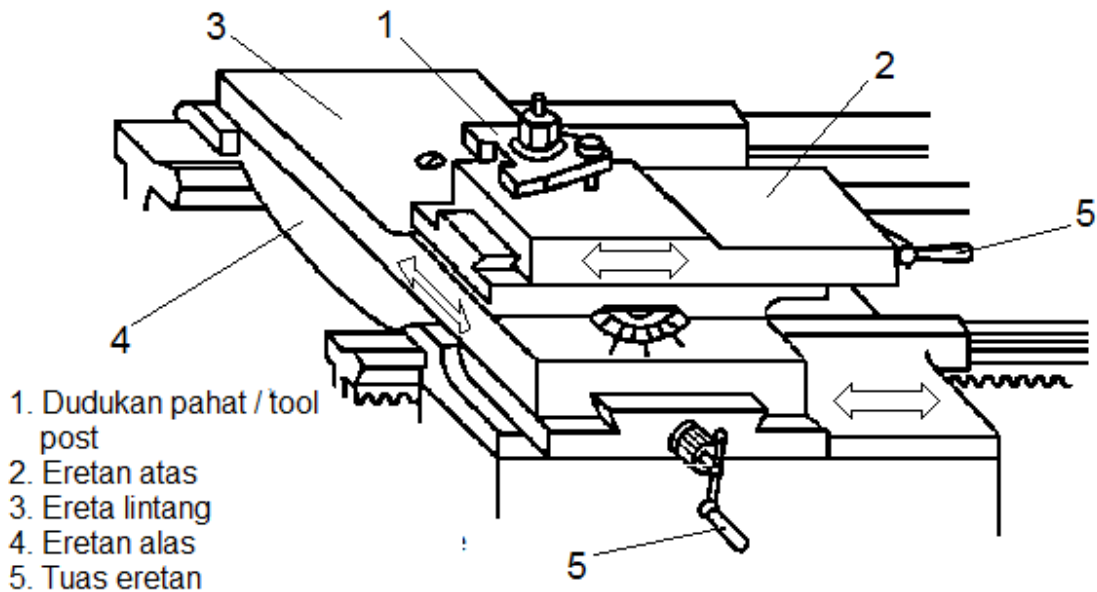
Komponen dari mesin bubut sliding dan screw cutting
